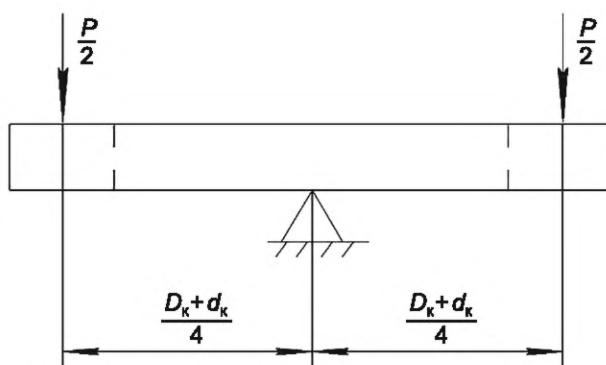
Схема приложения нагрузки к диску (пластине)
